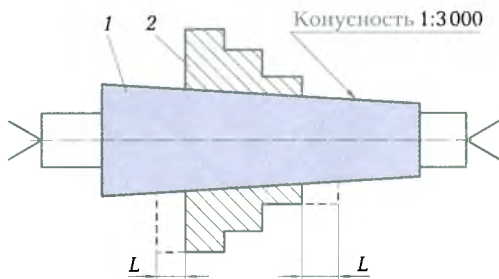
Схема установки детали с базовым отверстием на конусную оправку:
